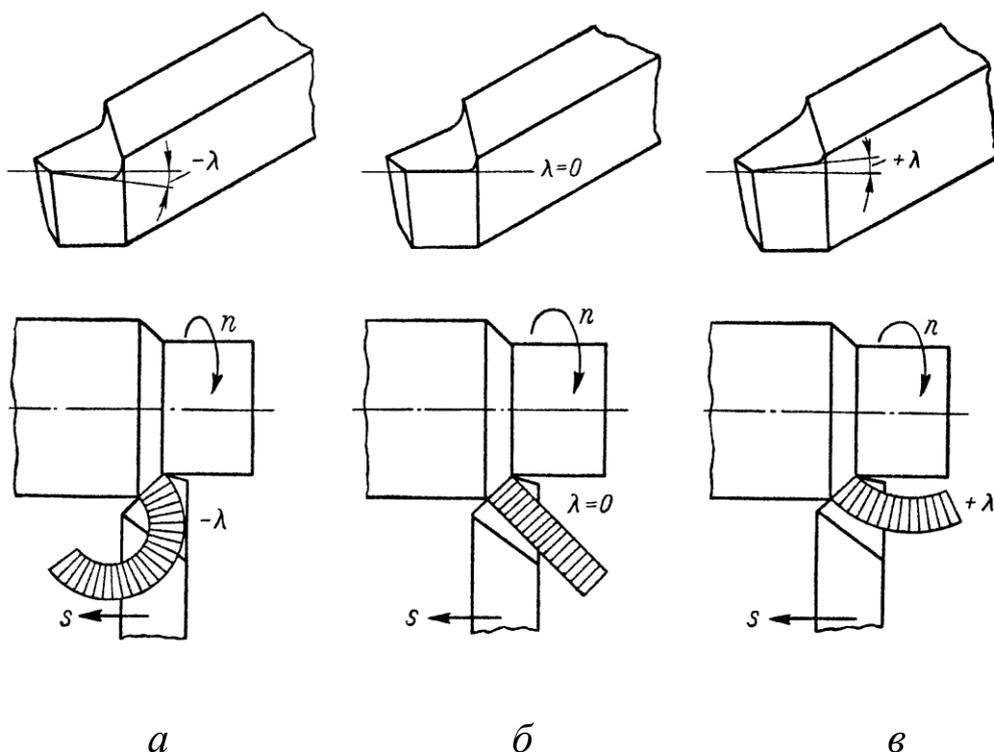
Угол наклона главной режущей кромки резца:
